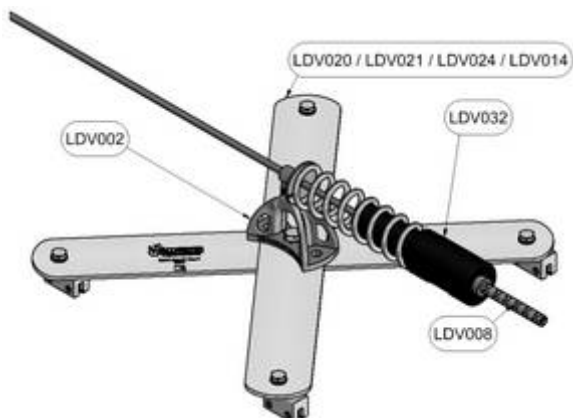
Montage ancre terminale avec absorbeur sur toiture à joints debout
